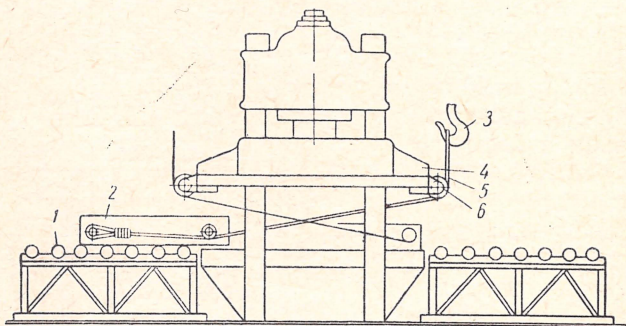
Приспособление для безопасной установки и съема тяжелых штампов
